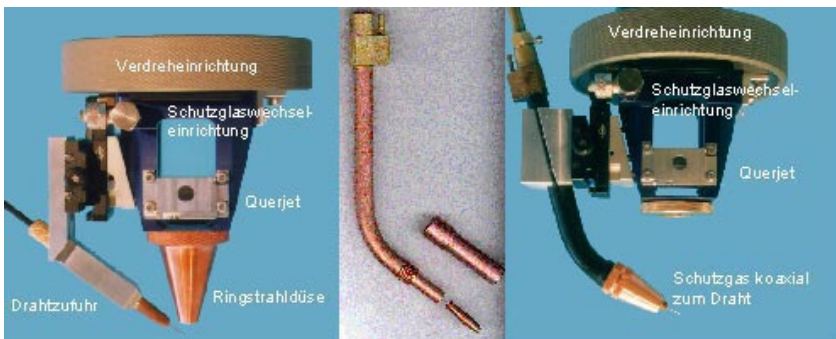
Modularer (gekapselter) Bearbeitungskopf zum Laserstrahlschweißen mit integrierter Schutzglaswechseleinrichtung und Querjet für  $f = 150 \text{ mm}$ ; links: Ringstrahldüse zur Schutzgaszufuhr; rechts: Schutzgaszuführung koaxial zur Drahtzufuhr; Mitte: modifizierter Pistoleneinsatz eines MIG-Brenners.
